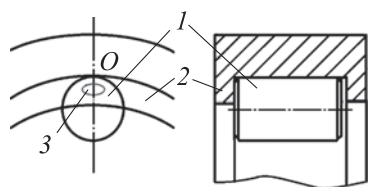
Схема контакта торцов ролика и борта наружного кольца цилиндрического роликоподшипника:
